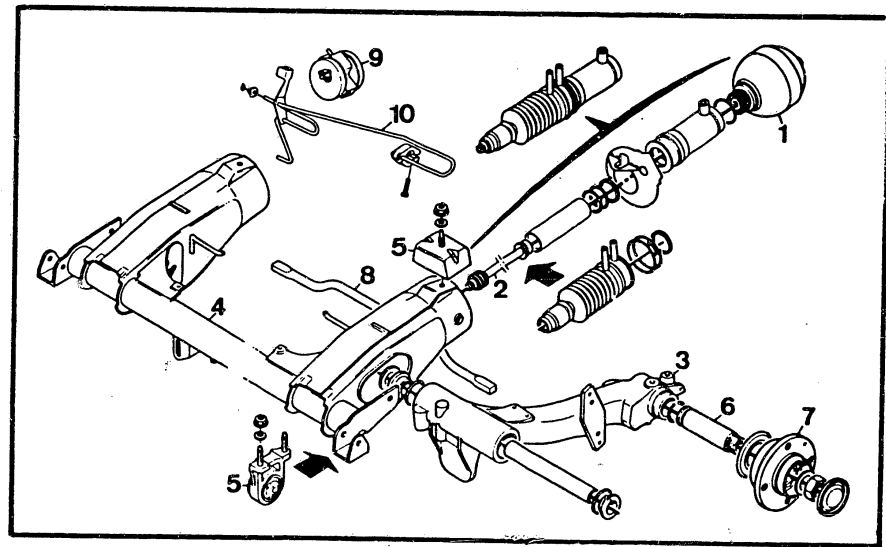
Elemente der Hinterradaufhängung. 1 Feder – 2 Kolben – 3 Längslenker – 4 Achskörper – 5 Lagerblock – 6 Bolzen – 7 Nabe – 8 Stabilisator – 9 Höhenregler – 10 Betätigungsgestänge.
